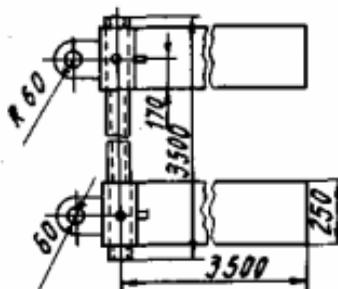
Чертеж полозы для транспортировки оборудования
